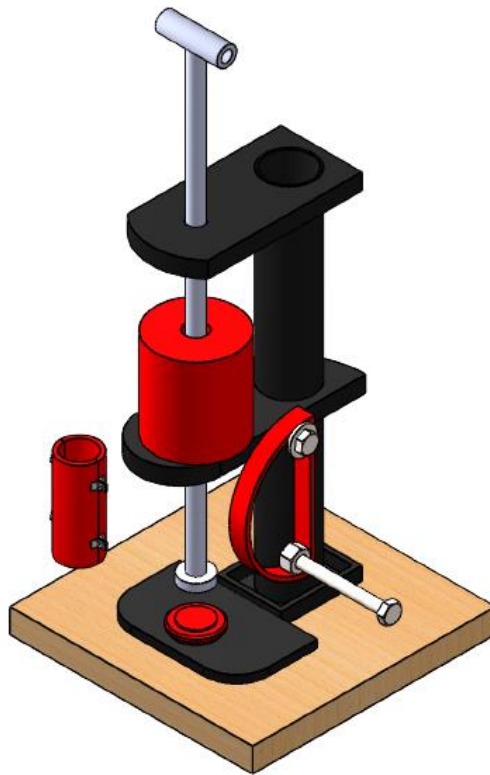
Ensamblaje Completo de Equipo Plug Maker.
